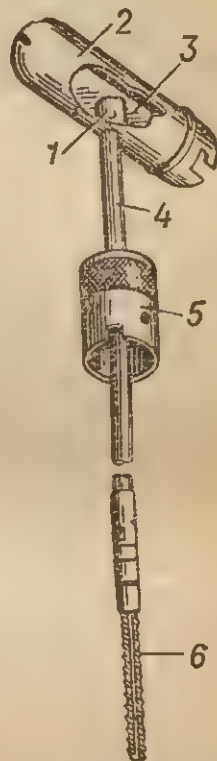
Принадлежность автомата, подготовленная для чистки: 1 — головка шомпола; 2 — пенал; 3 — отвертка; 4 — шомпол; 5 — крышка пенала; 6 — протирка
